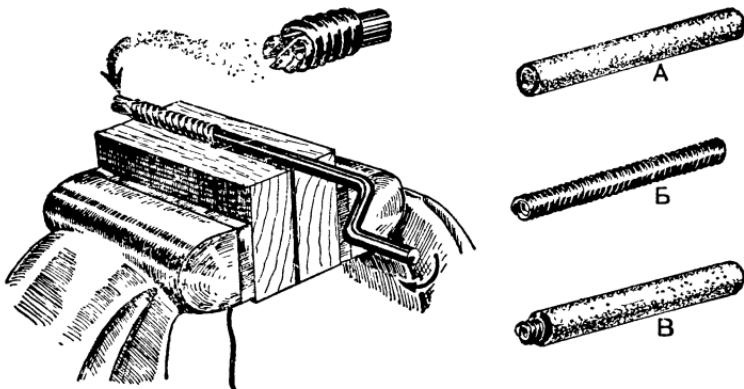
Гибкие валы. Слева — навивка спиральных пружинок воротком; справа — конструкции гибких валов: А — резиновая трубка; Б — спиральная пружинка; В — пружинка в трубке.
